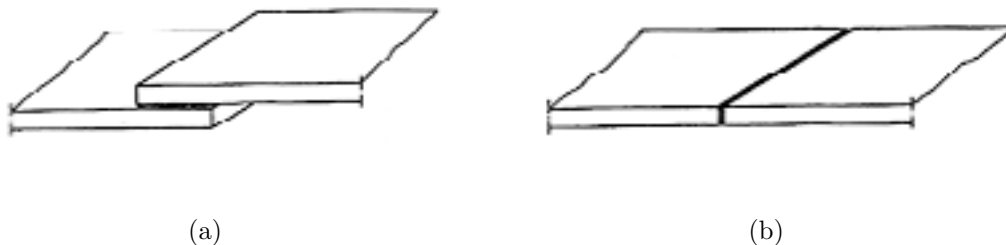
Configuration des principaux types de joints : par recouvrement (a) et bout à bout (b)
